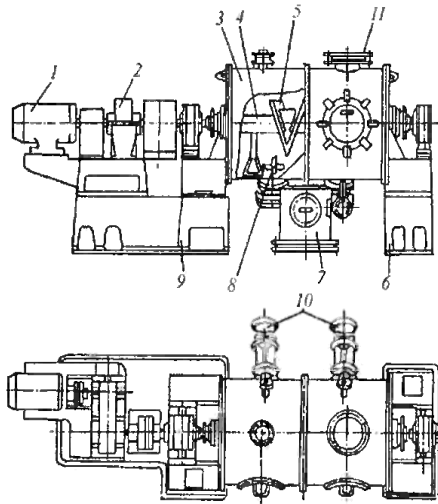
Плужний змішувач: 1 – електродвигун; 2 – редуктор; 3 – корпус; 4 – вал; 5 – лопаті-плуги; 6 – опора корпусу; 7 – розвантажувальна коробка; 8 – ножова головка; 9 – станина; 10 – привід ножової головки; 11 – люк
